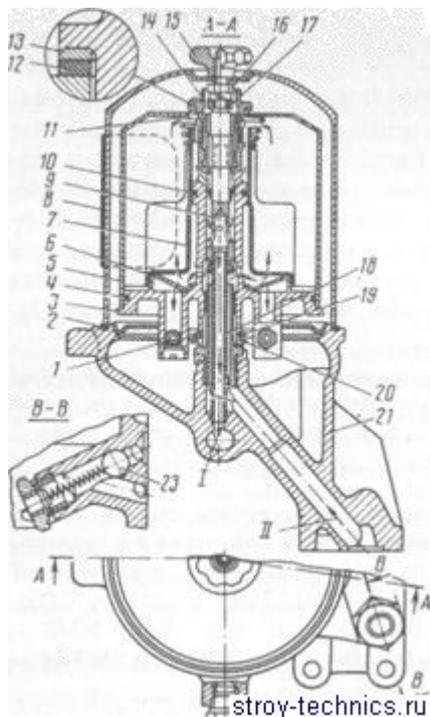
Центробежный масляный фильтр (полнопоточная центрифуга) двигателей ЗИЛ-130, -375ЯТ, -375Я5:
